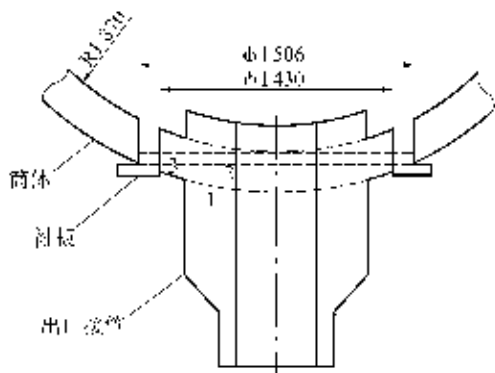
接管马鞍形焊缝坡口形式结构简图
